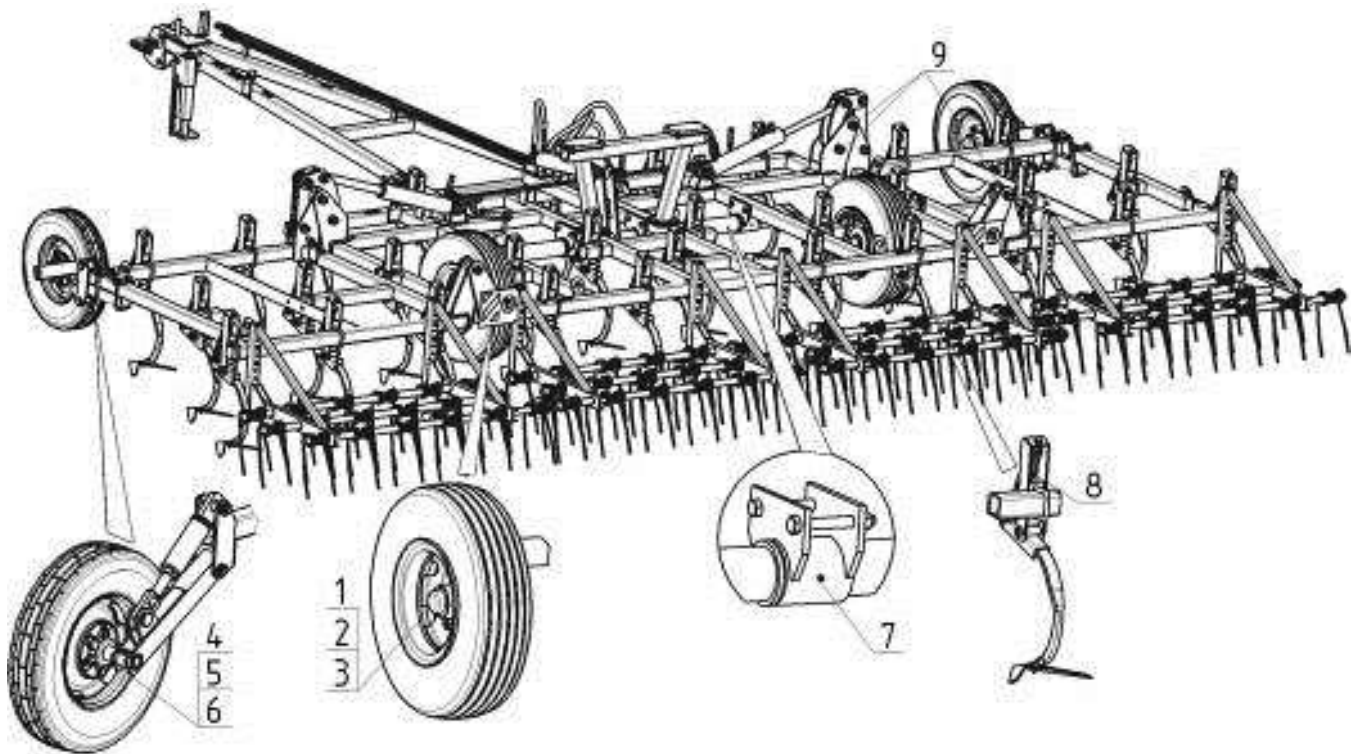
Места смазки. Схема расположения подшипников и манжет
